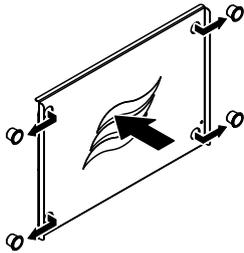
Stopfen im Befeuchtergehäusedeckel entfernen
